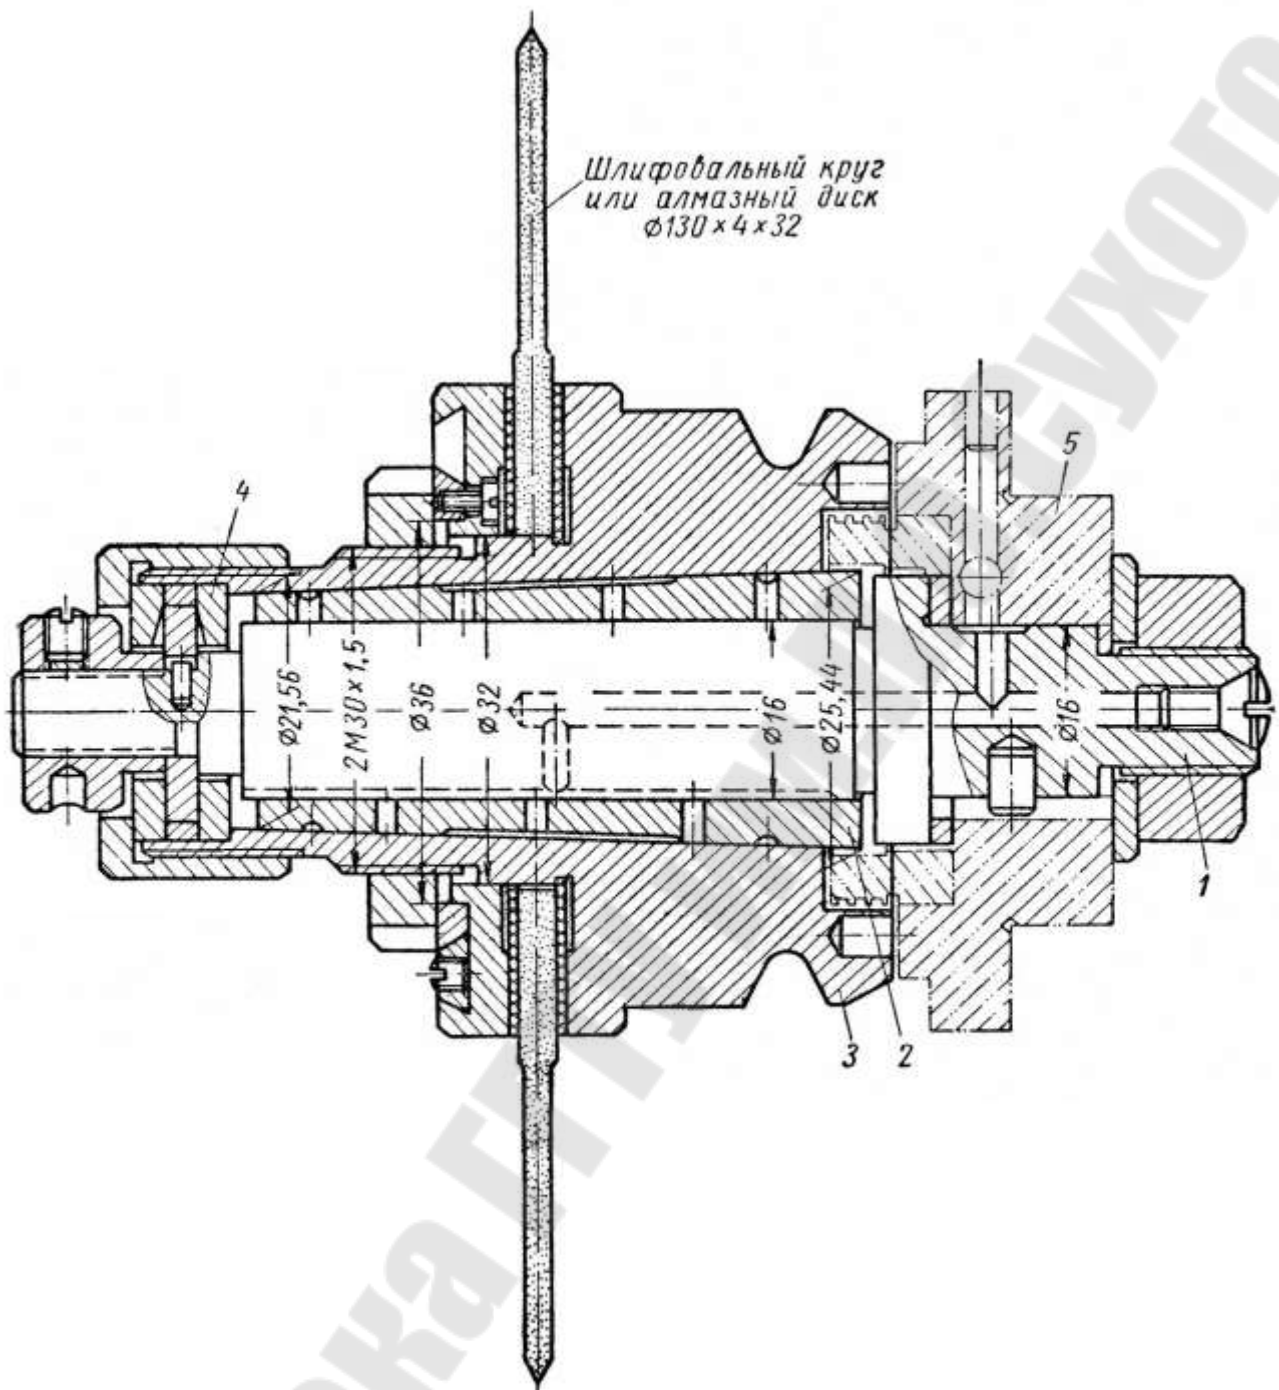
Эскиз шлифовального шпинделя станка модели Ш-228
